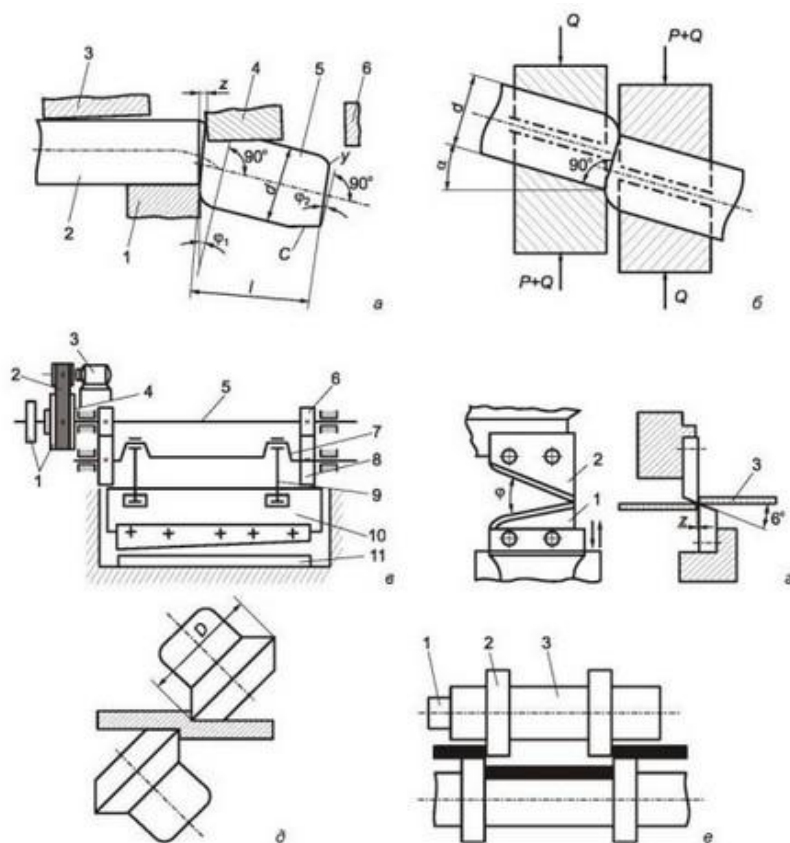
Схеми різки металопрокату на ножицях
